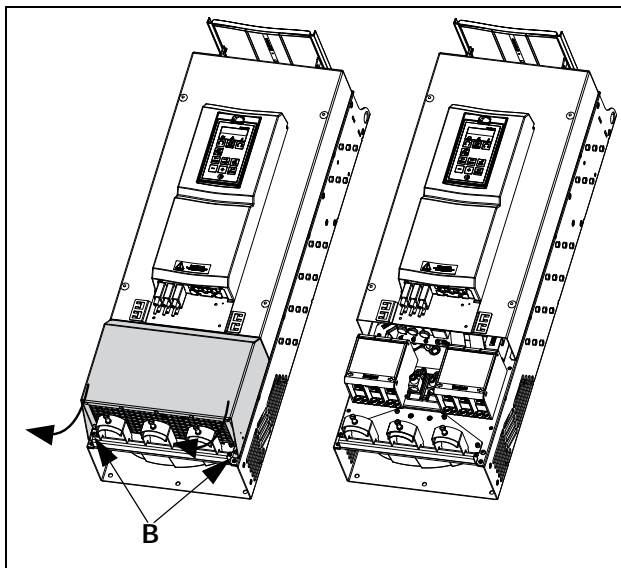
Lösen Sie die beiden Schrauben, und entfernen Sie die untere Abdeckung (Prinzipzeichnung).
